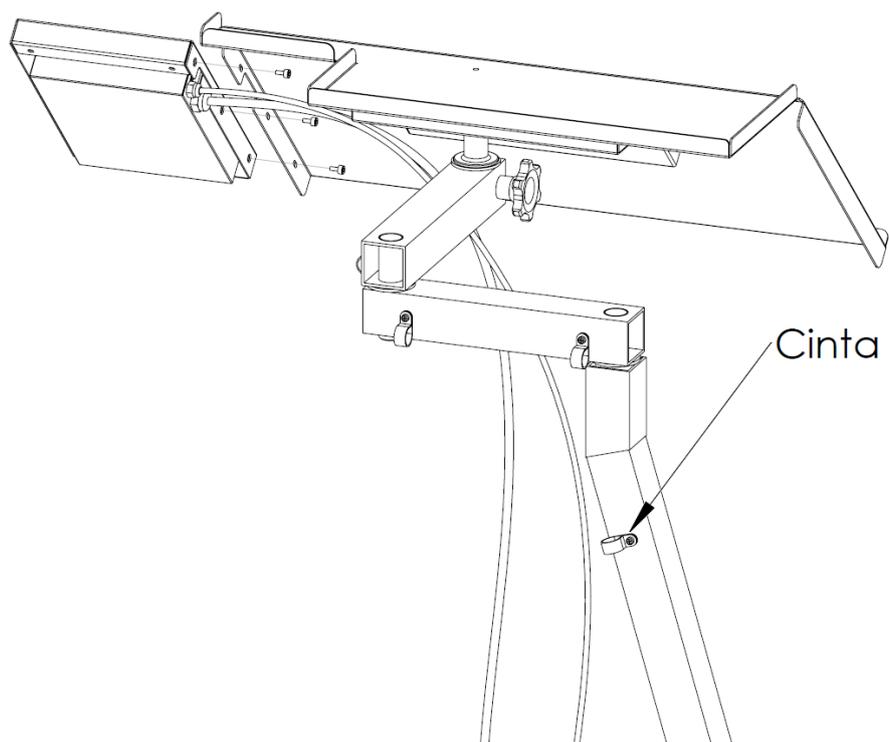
Montagem Final do Suporte do Computador e do Painel de Controle
